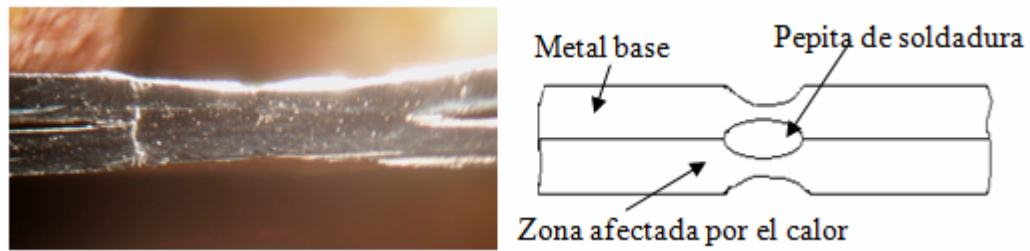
Vistas transversales de la penetración de la soldadura
